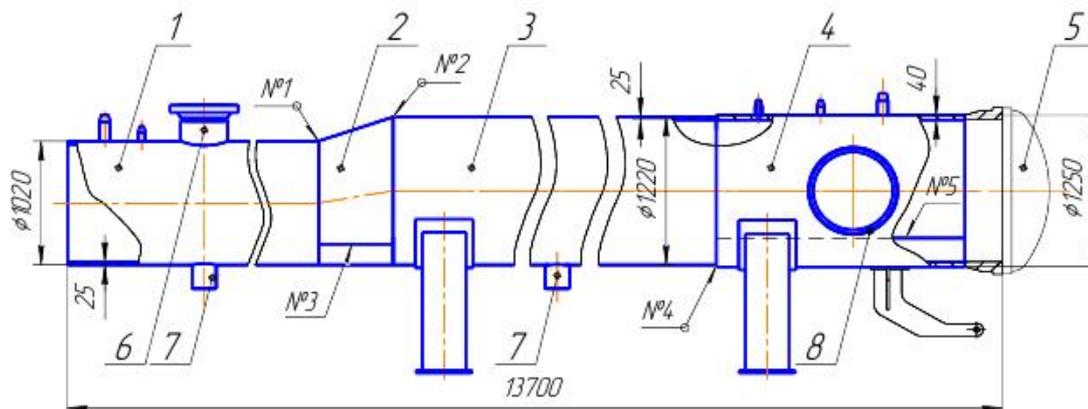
Общий вид корпуса камеры запуска СОД
